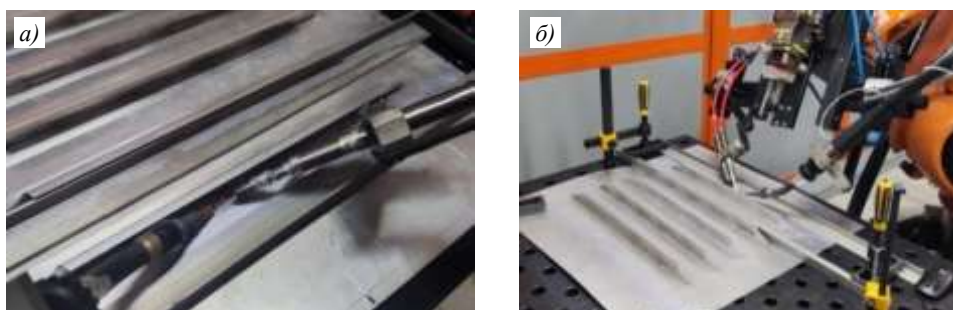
Расстановка прихваток (а) и общий вид конструктивно-подобных образцов стрингерных панелей на роботизированном комплексе Laser Weld 8R60 (б)
